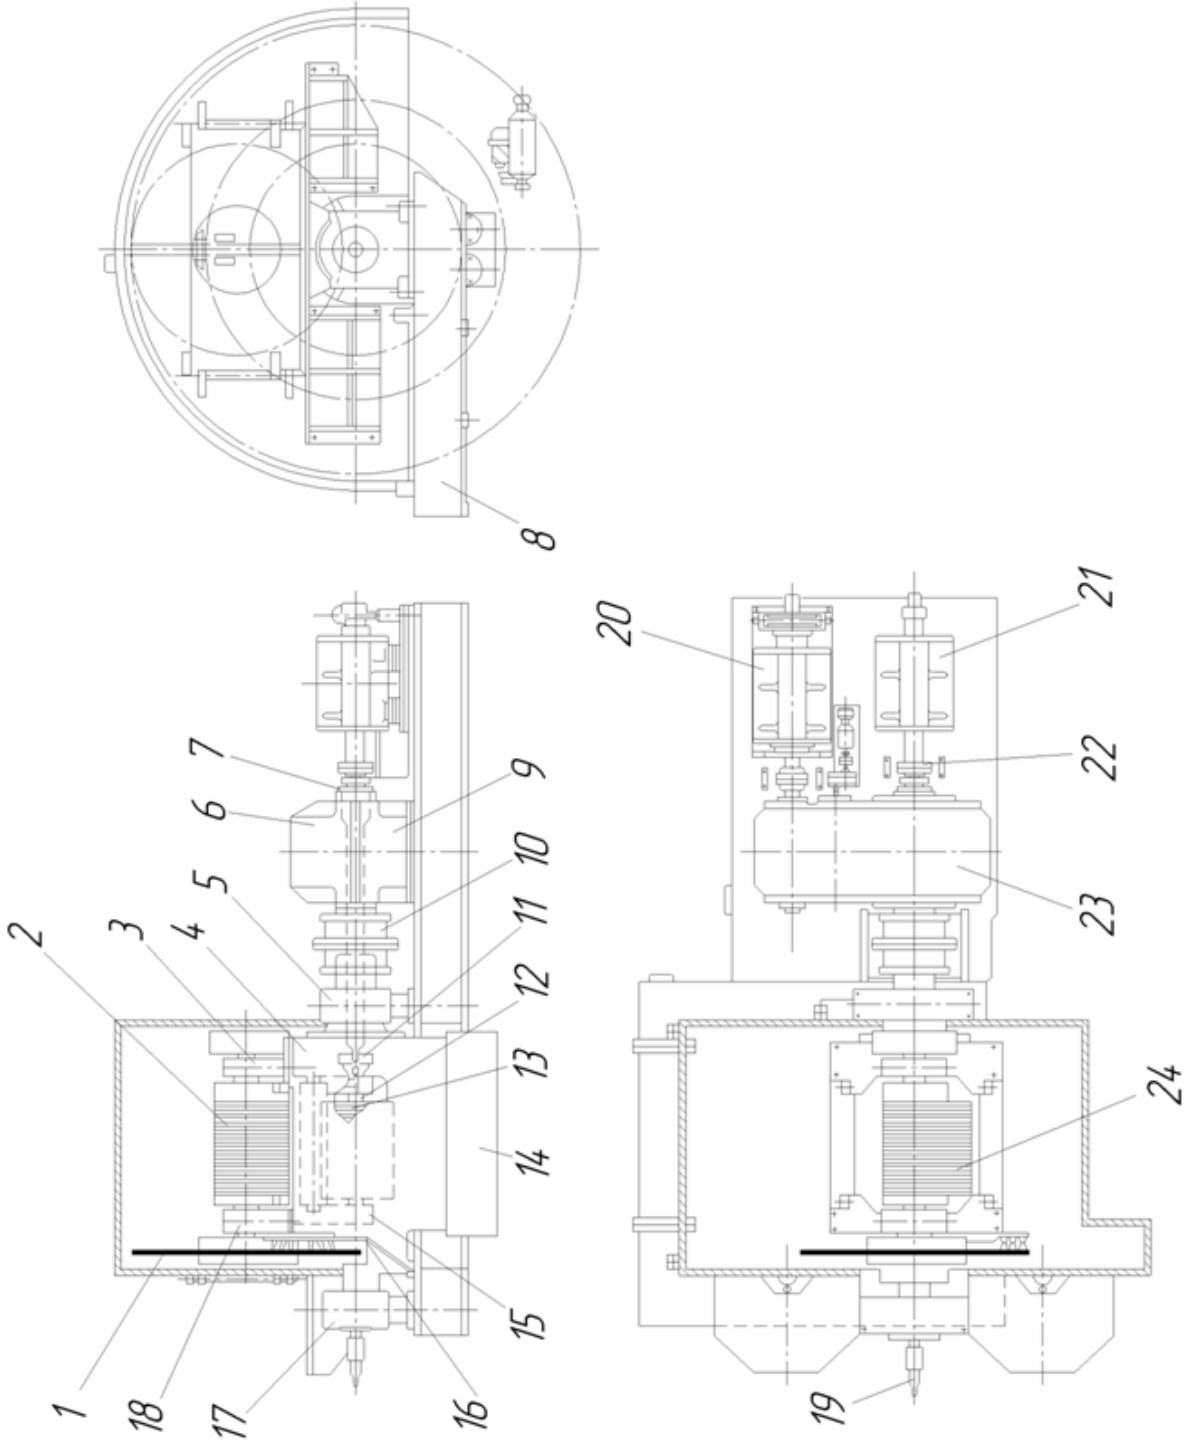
Конструкція роторної пили РР 2500/2000
